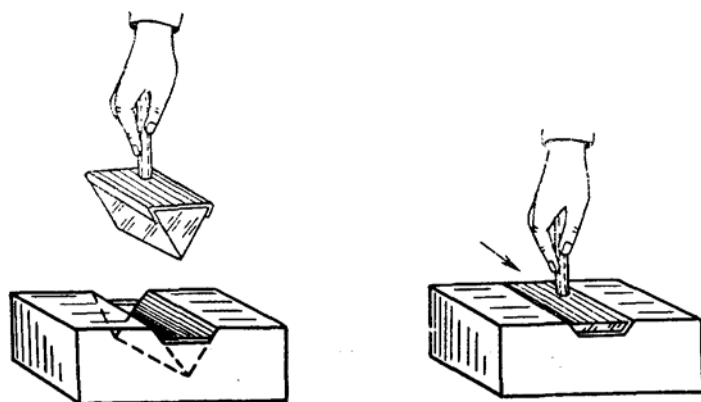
Приспособление для проверки прочности вклейки призм в оправу.
